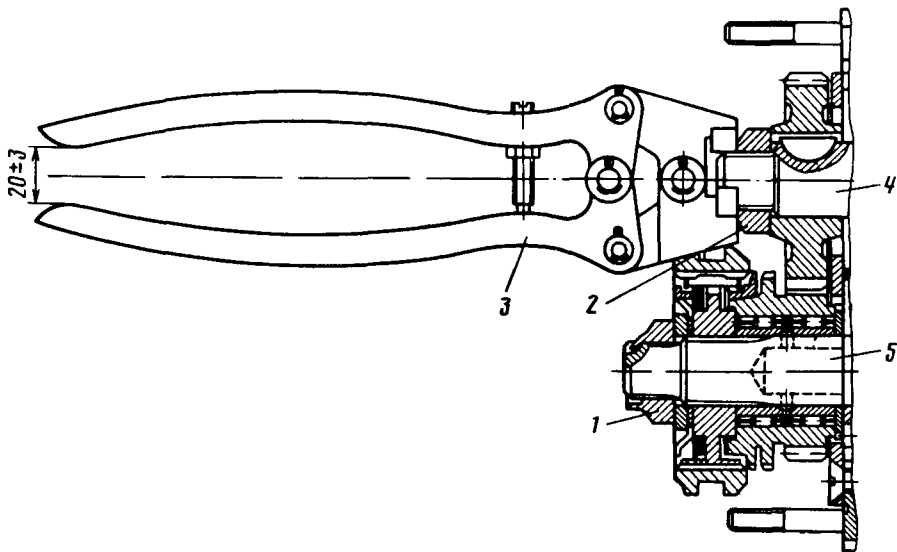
Стопорение гаек ведущего и ведомого валов коробки передач:
